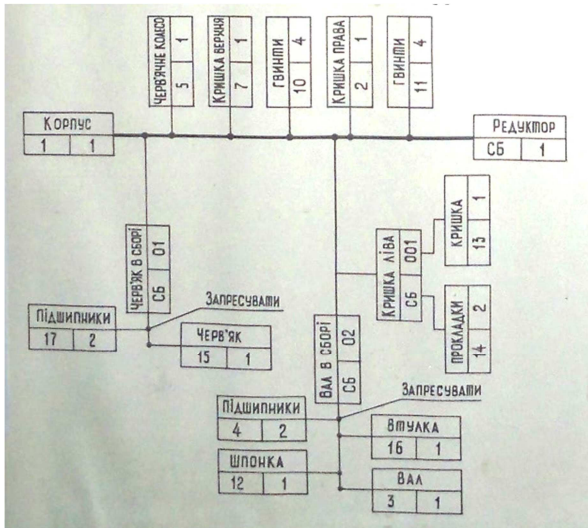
Технологічна схема складання вузла «корпус – вал – червячне колесо» червячного редуктора
